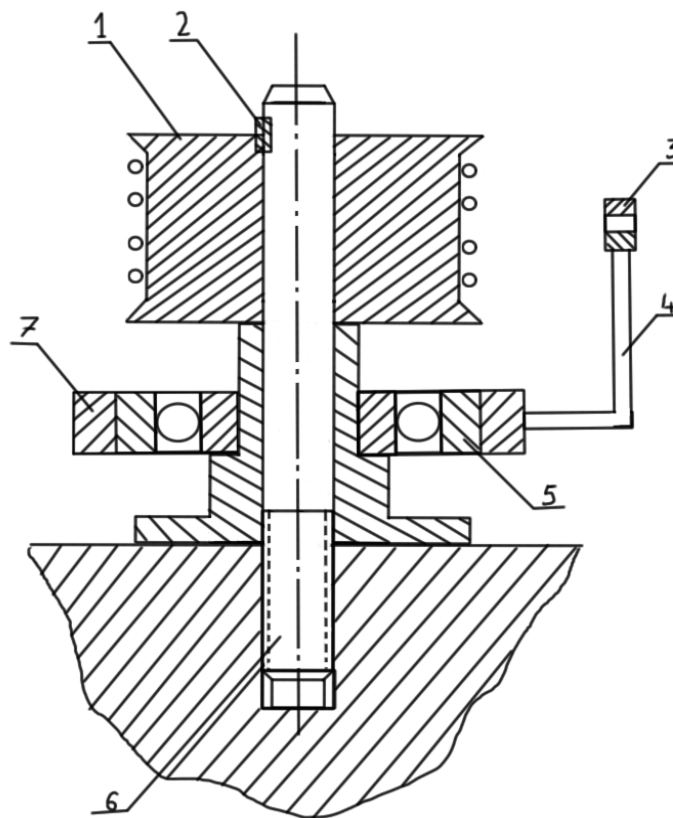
Механизм сматывания металлической нити с катушки
